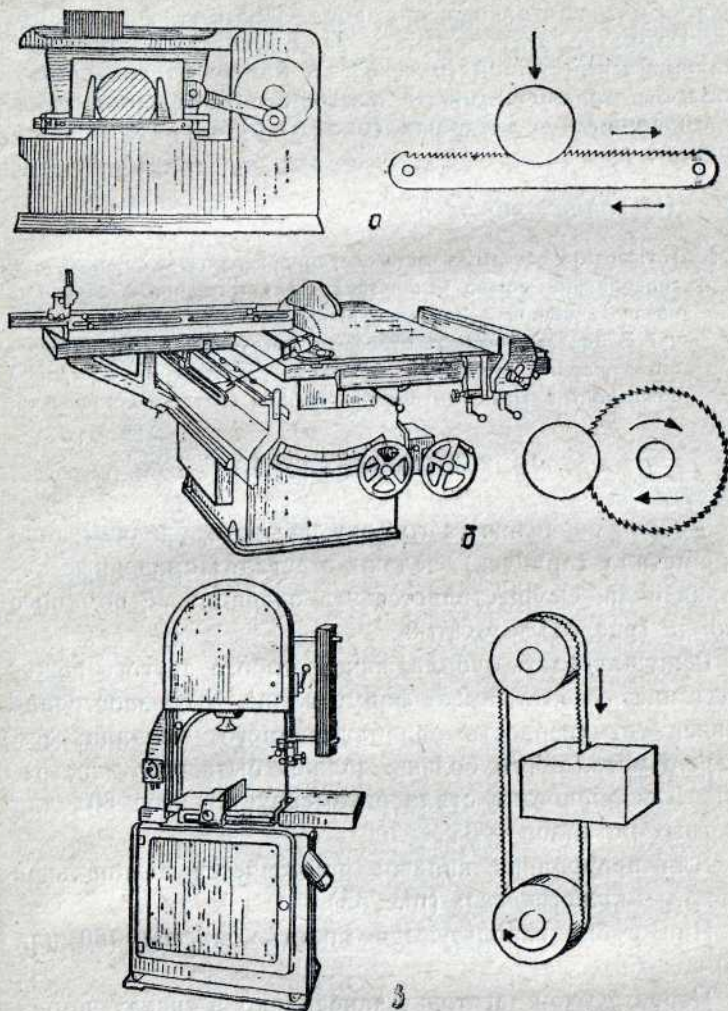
Пиление заготовок из сортового проката в промышленном производстве: а — механической пилой; б — дисковой пилой; в — ленточной пилой.
